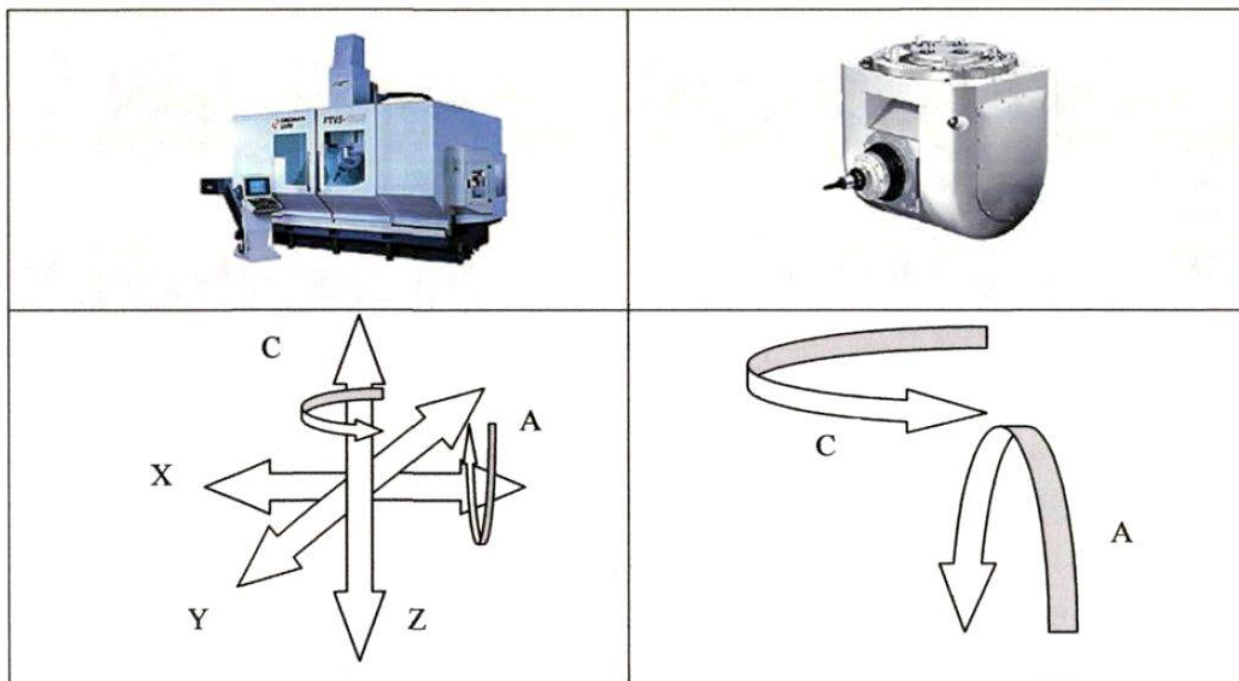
Вертикальний 5-ти координатний верстат мод. FTV5 фірми Cincinnati Machine Ltd.
